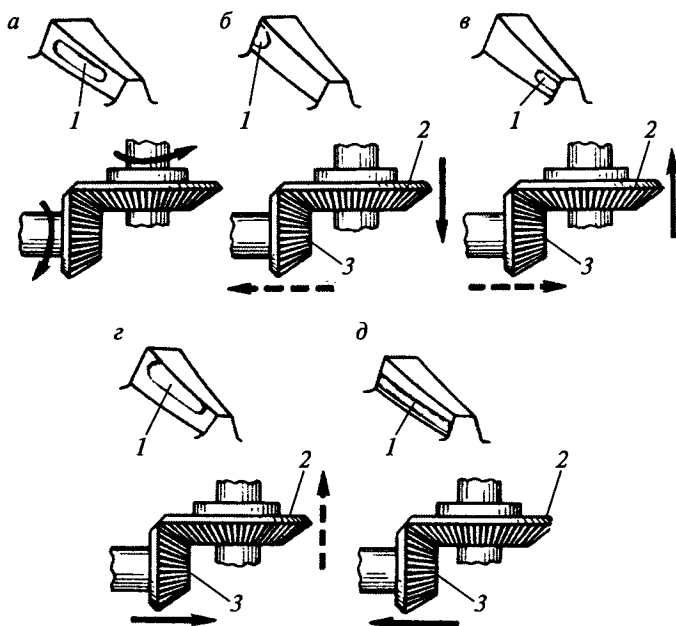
Схемы регулирования зацепления конических шестерен главной передачи
